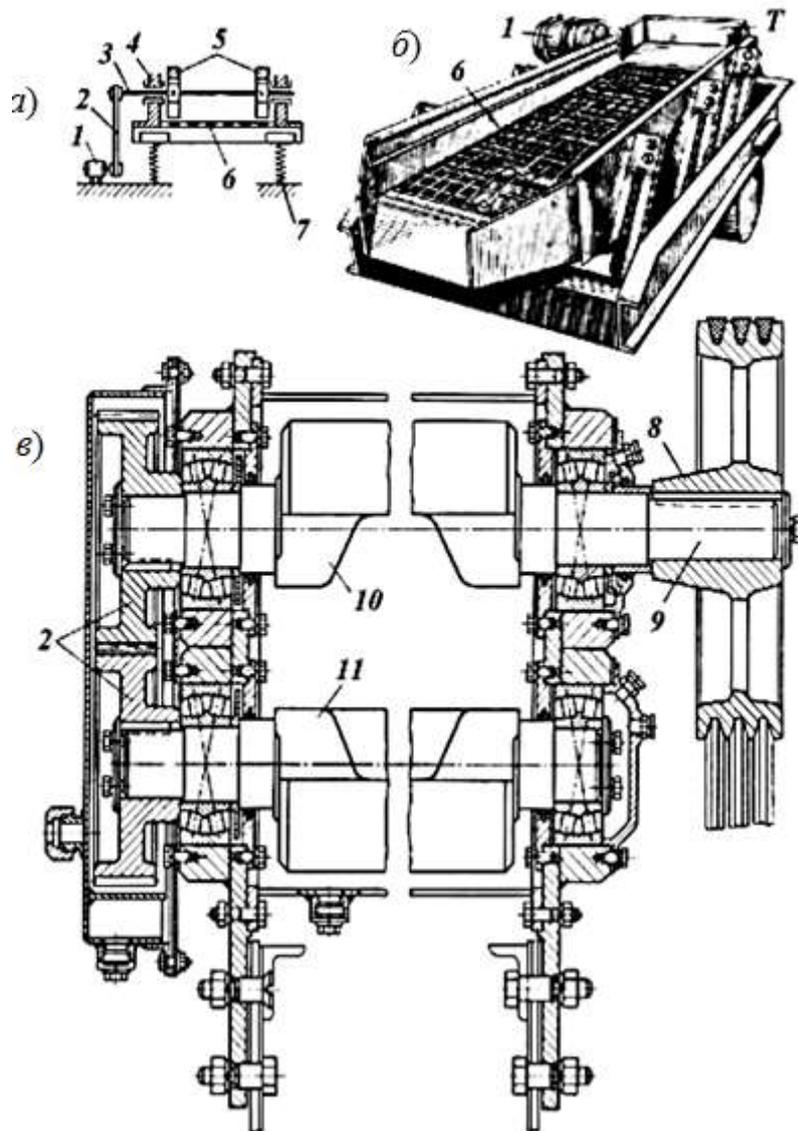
Вибрационный грохот: а – схема грохота; б – общий вид; в – разрез вибратора; *T* – зона загрузки; 1 – электродвигатель; 2 – ремень 3 – вал; 4 – рама; 5, 10 и 11 – дебалансы; 6 – сито; 7 – пружины; 8 – шкив; 9 – вал дебаланса; 12 – шестерня.
